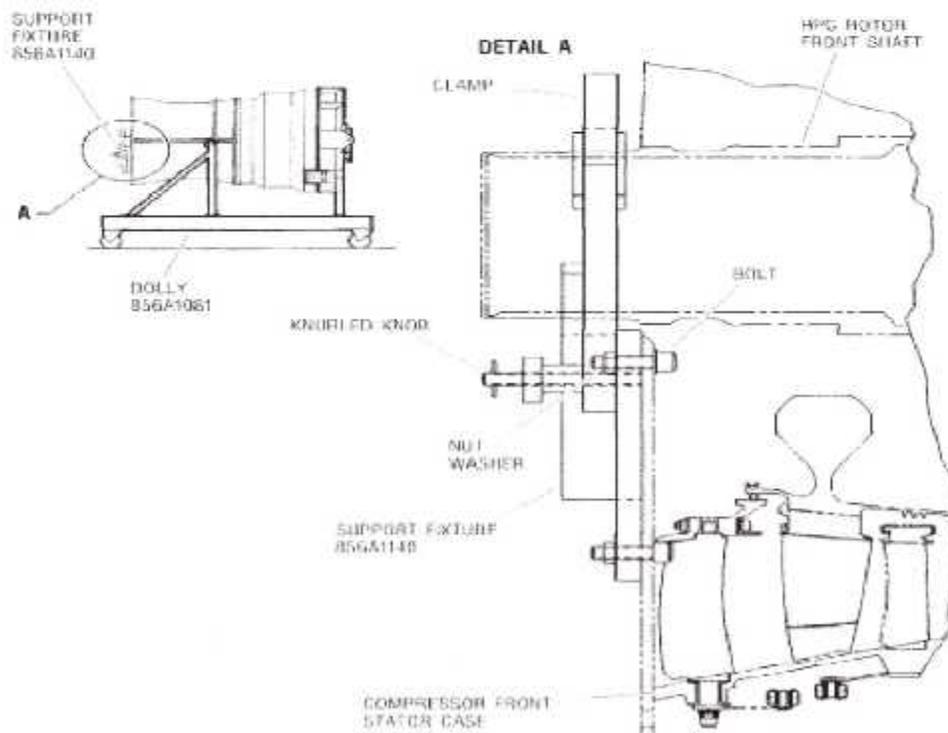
Enlèvement du Dispositif, 856A1140G06 de la Partie Avant du l'Arbre du Rotor de la HPC.
